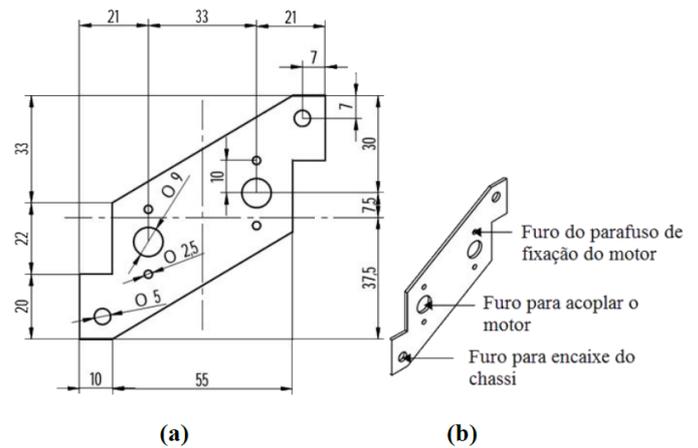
(a) Dimensões do Suporte do Motor, valores em milímetros. (b) Esquema do Suporte do Motor.
